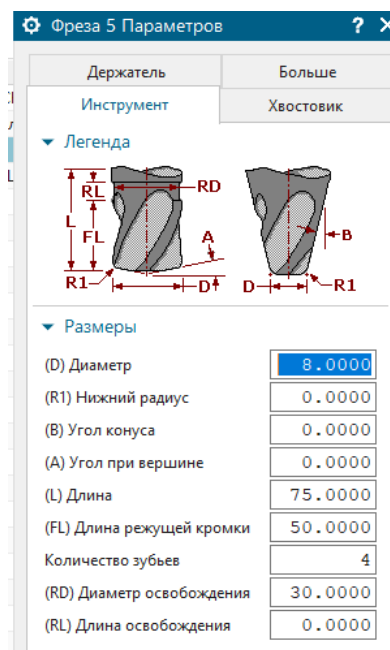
Ріжучий інструмент – фреза кінцева
